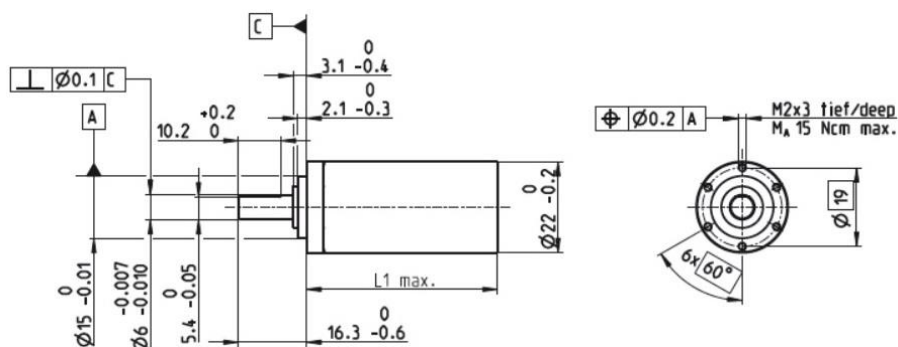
Dimensões do redutor Maxon Planetary Gearhead GP 22 HP
